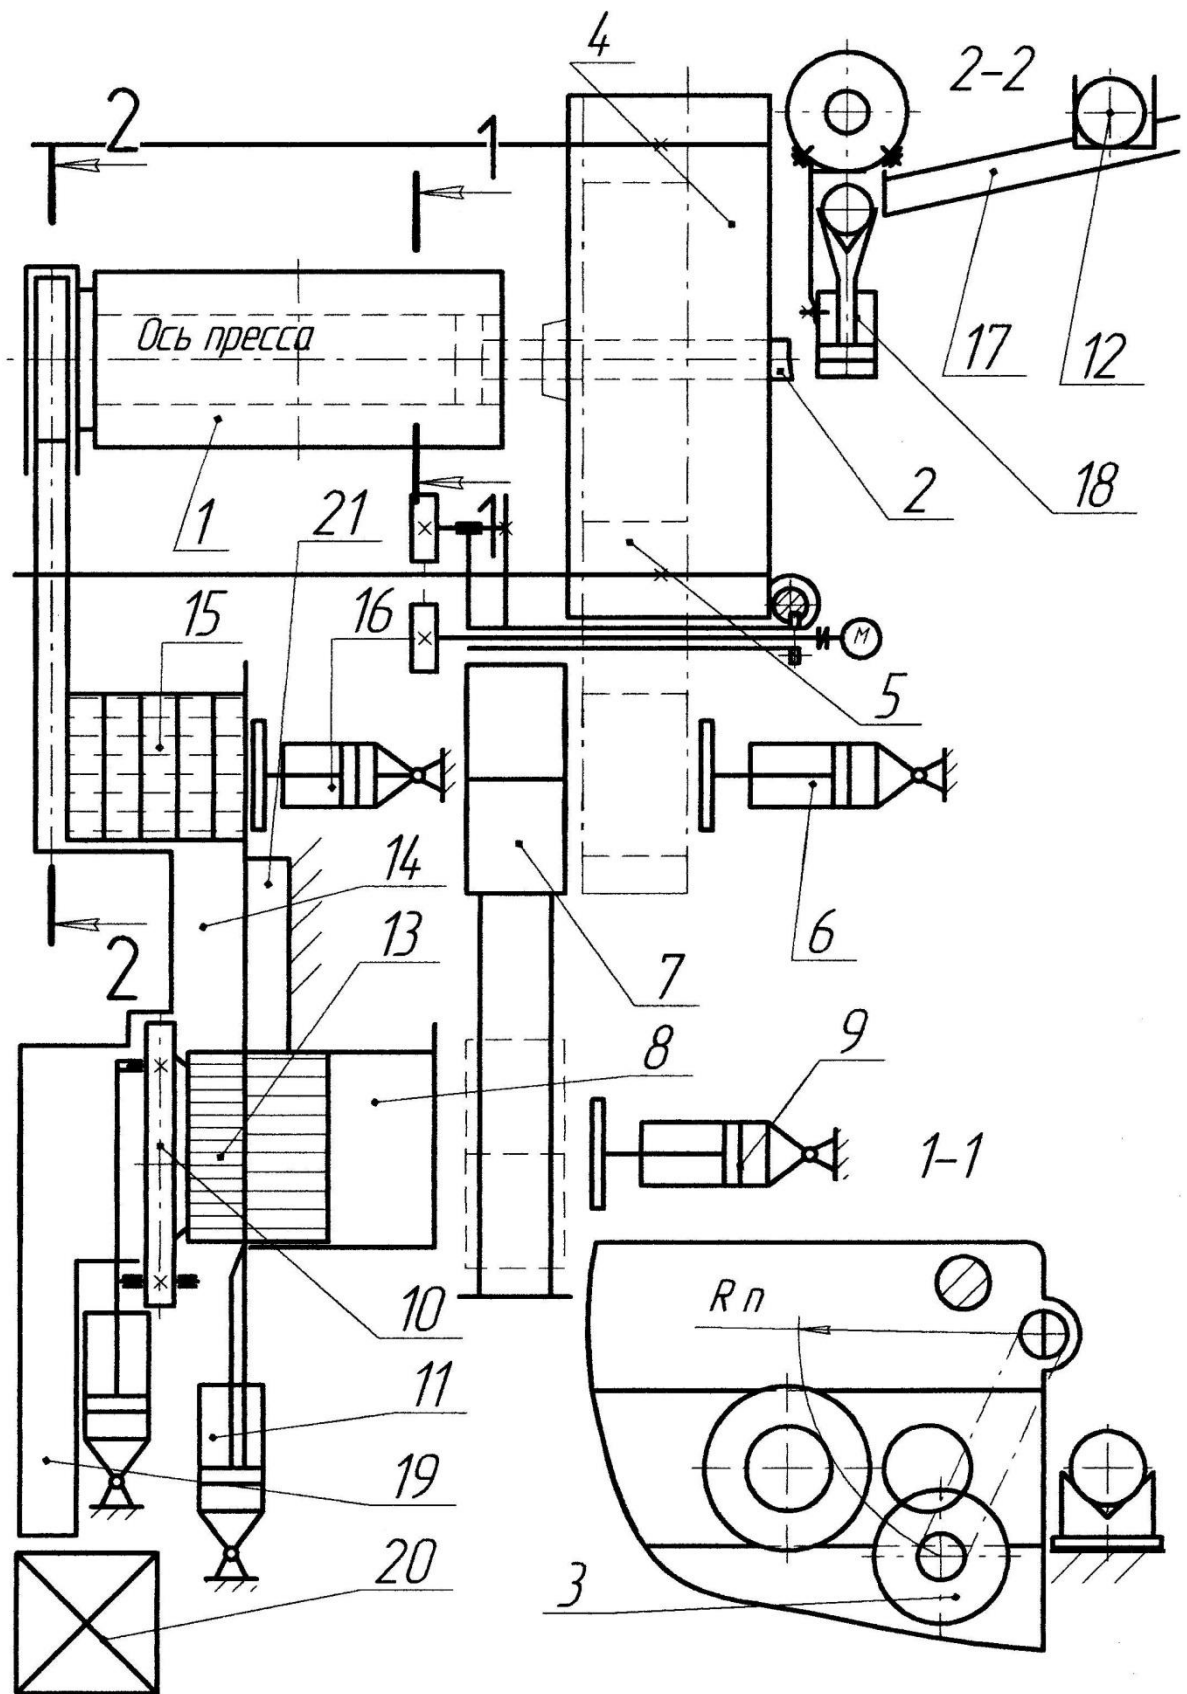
Схема відділення прес-залишку і обробки прес-шайби
